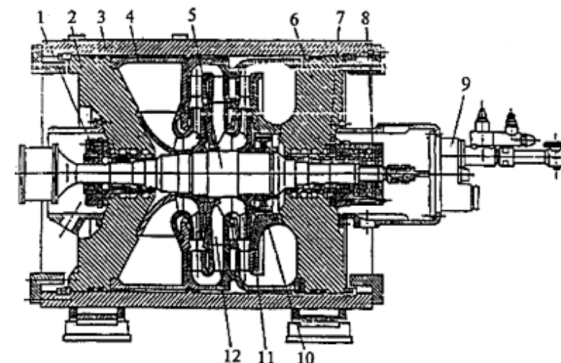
Полнонапорный двухступенчатый нагнетатель НЦ-16/76 агрегата ГПА У16
